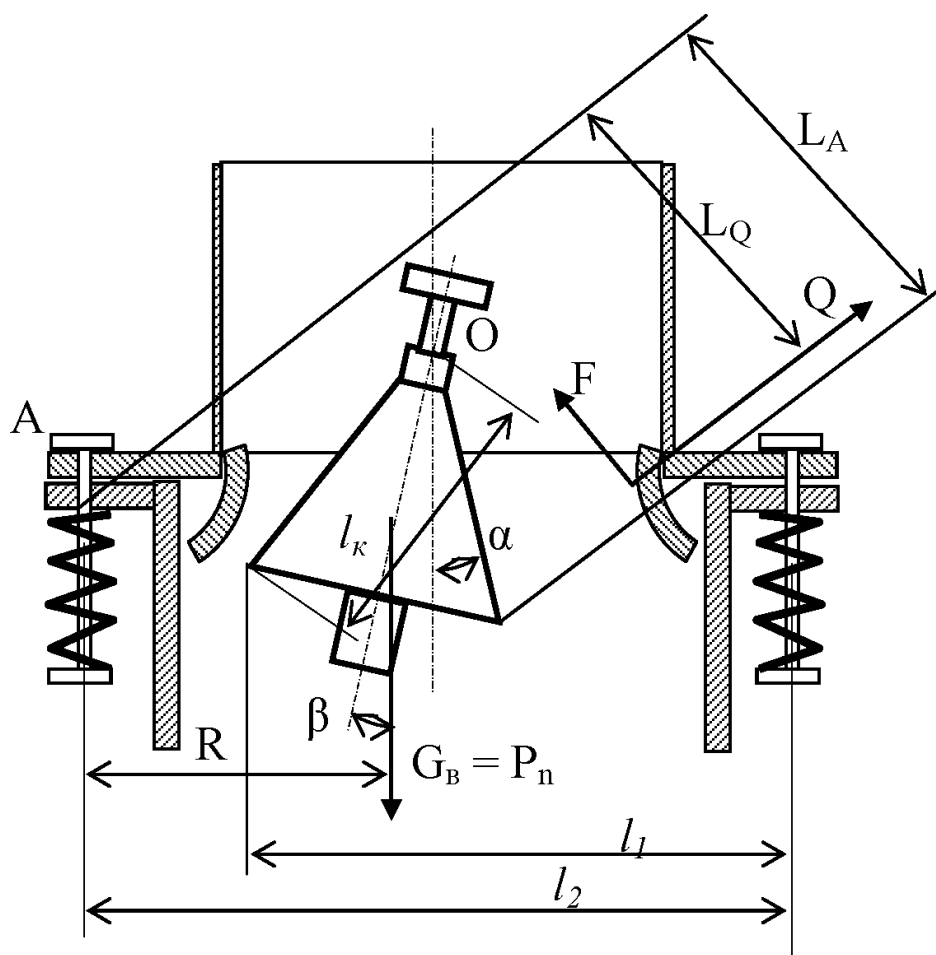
Рівновага верхньої частини дробарки під дією зовнішніх сил [4-15, 17-19].
